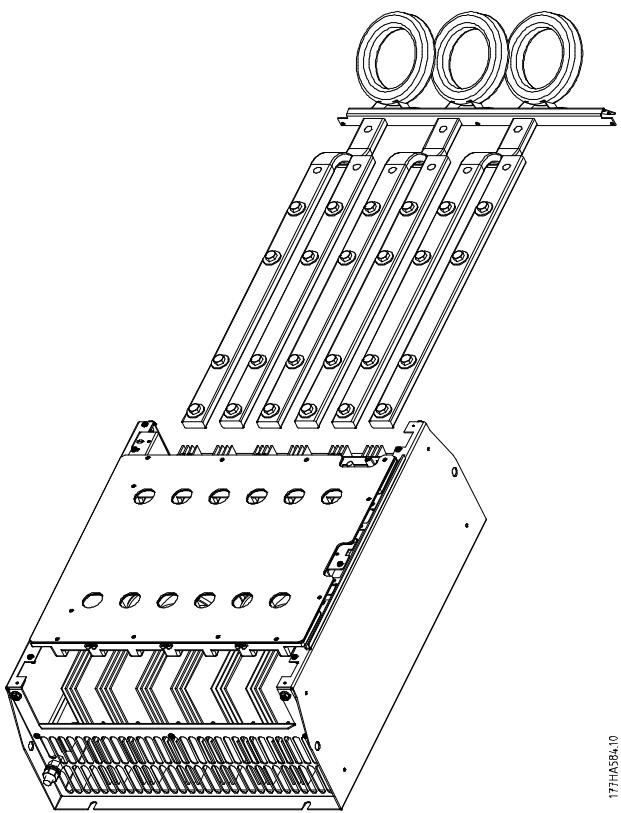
Barras condutoras com braçadeiras para cabos
